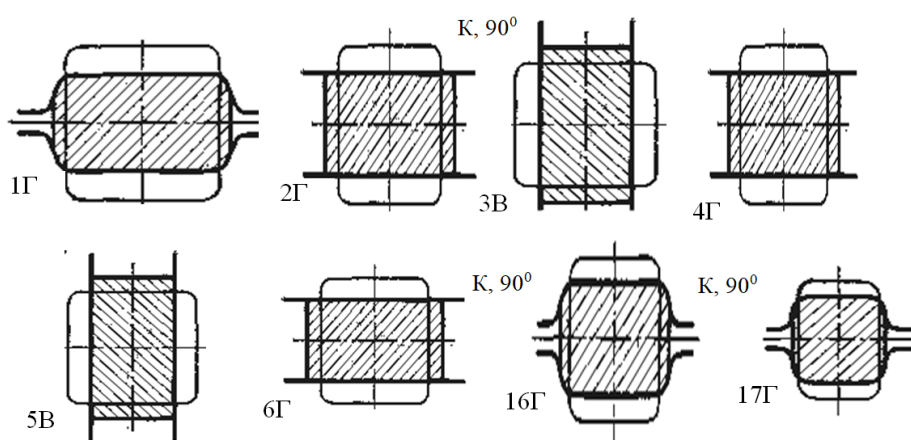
Предлагаемая для крупносортного стана «600» система «ящичный калибр — гладкая бочка»
